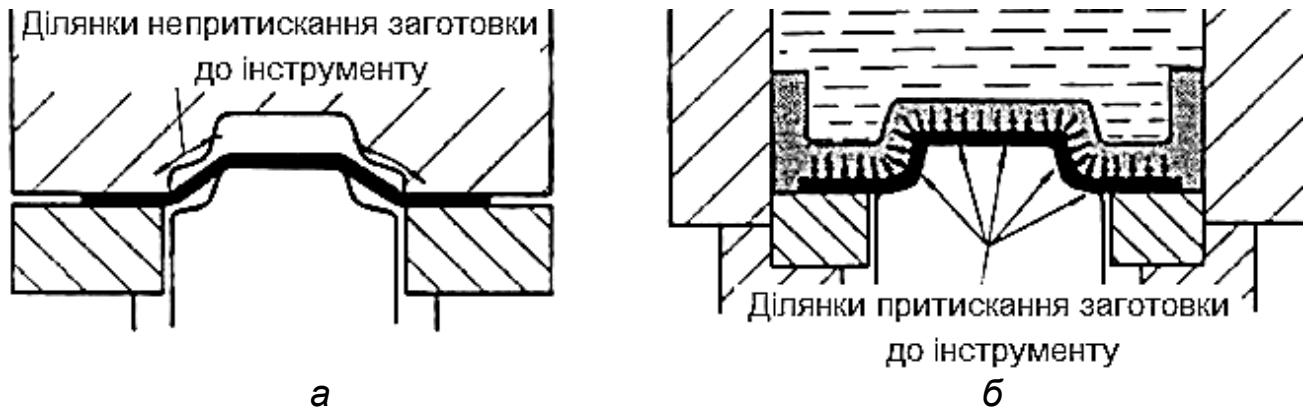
Схема прикладення деформувальних зусиль до заготовки у двох варіантах формоутворення:
